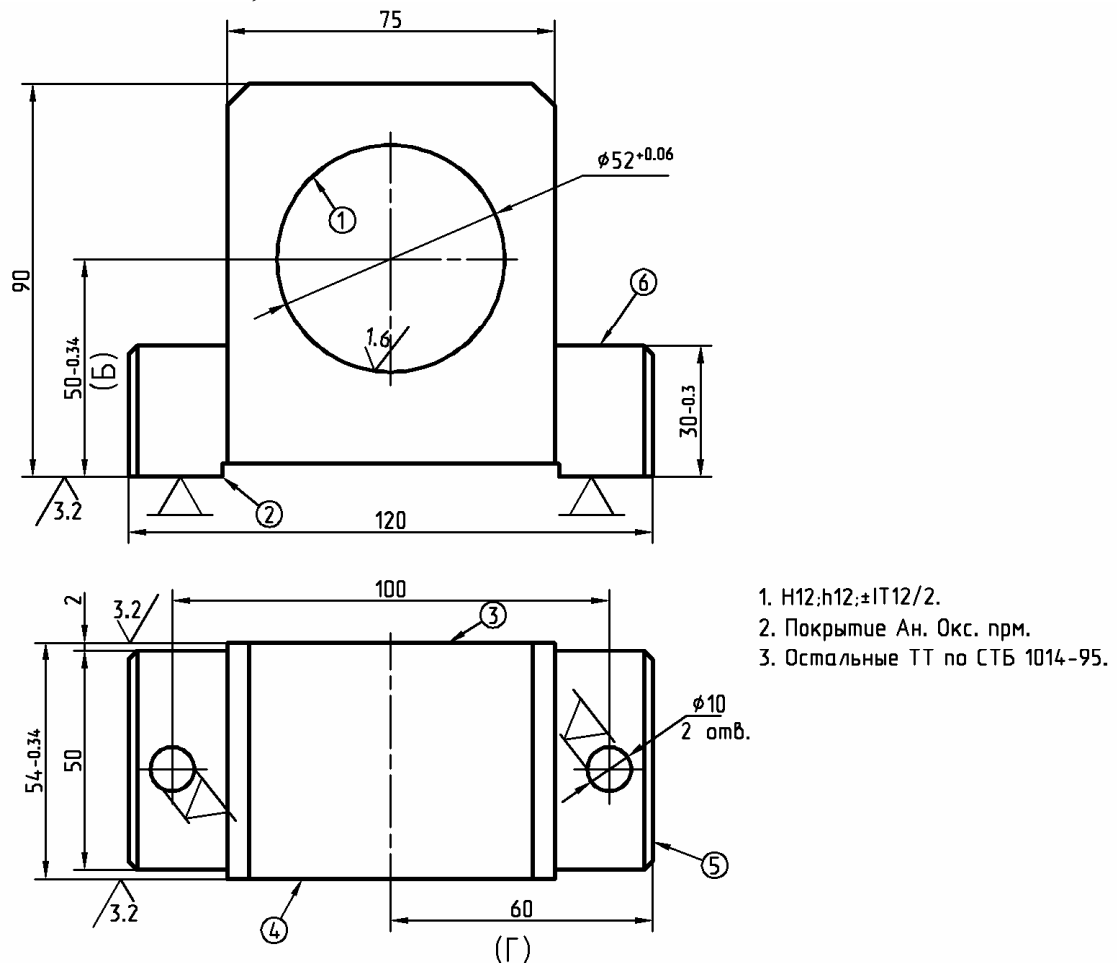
Корпус подшипника: чертеж и схема установки при обработке отверстия $\varnothing 52^{+0,06}$ мм
